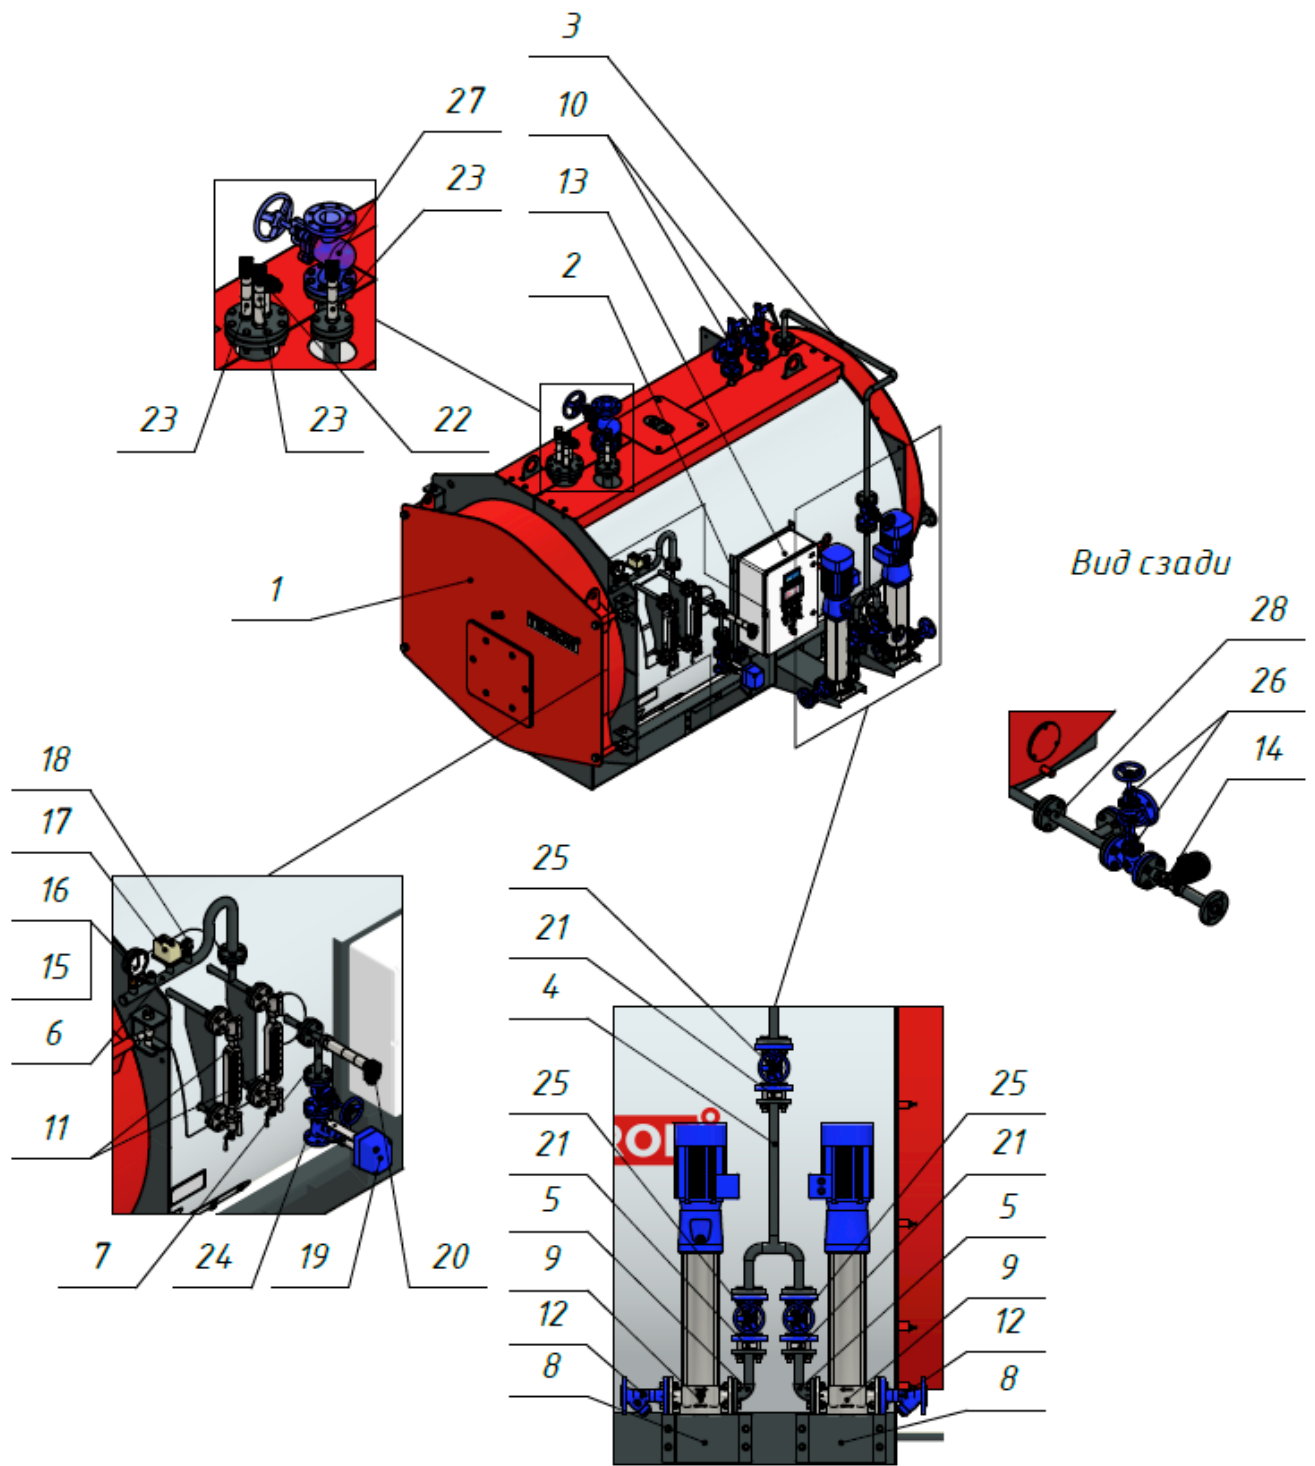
Схема установки дополнительного оборудования парового котла TEMRON SL
